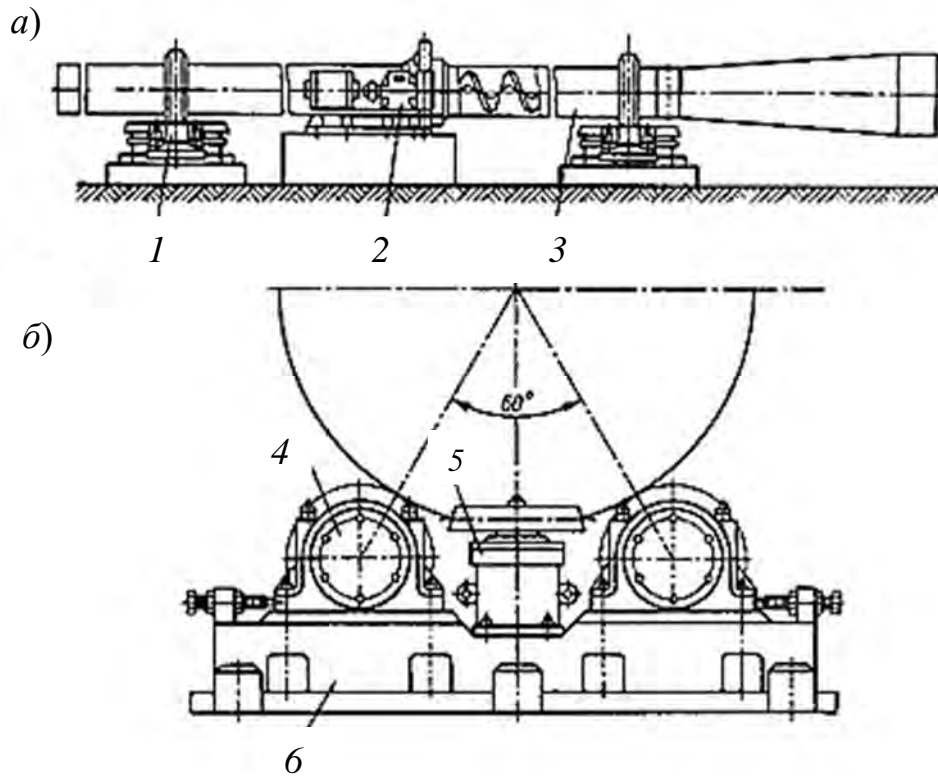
Конструктивная схема винтовой транспортирующей трубы: *а* – общий вид; *б* – опорная рама с роликами; 1 – опорно-упорный узел; 2 – привод; 3 – труба; 4 – опорный ролик; 5 – упорный ролик; 6 – рама
